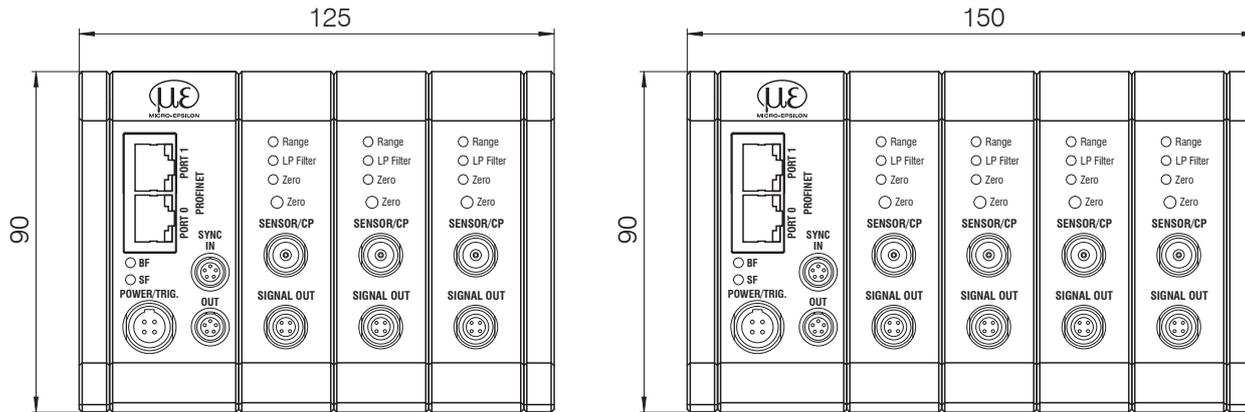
Maßzeichnung Controller mit drei oder vier Demodulatormodulen.
